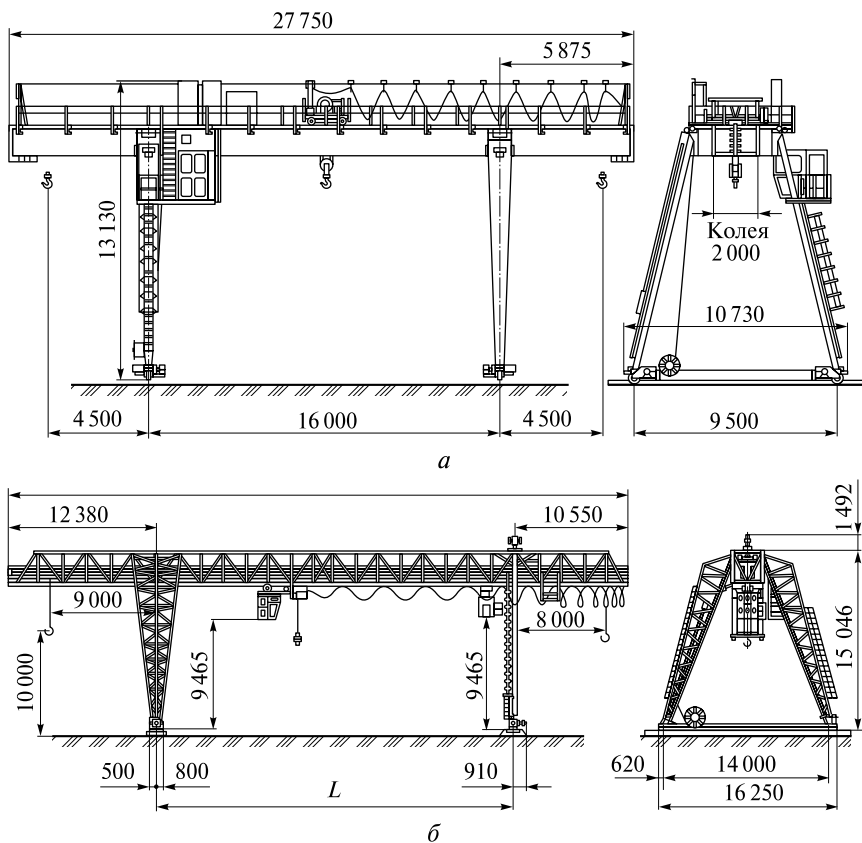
Козловые краны из фасонных прокатных стоек и балок (а), решетчатой конструкции (б):
